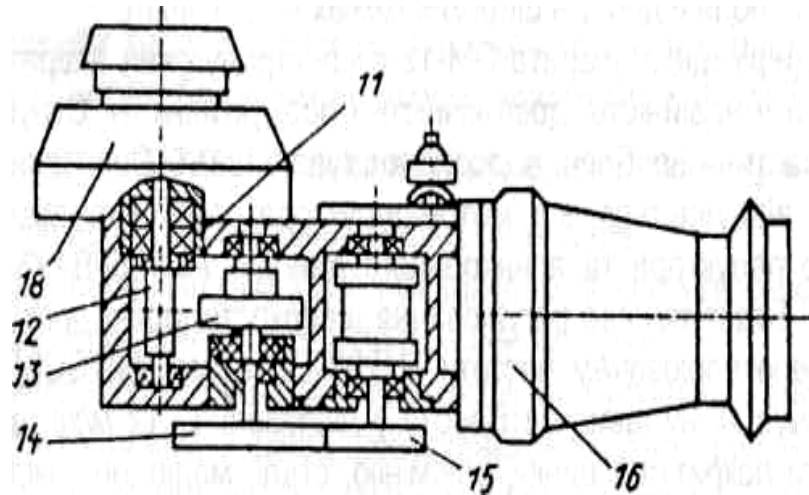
Схема електродугового металізатора ЕМ-14М
